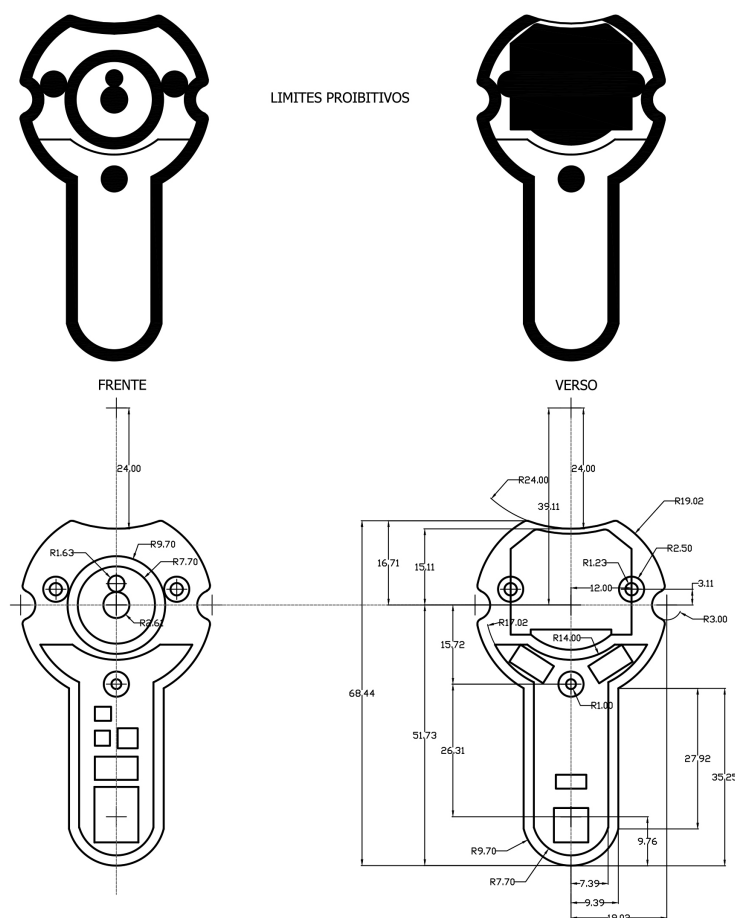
Desenho CAD da placa de circuitos impressos com os limites proibitivos e as dimensões.
